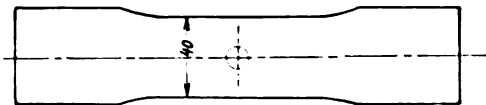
B. Stäbe mit zylindr. Bohrungen 10 mm Dmr.
